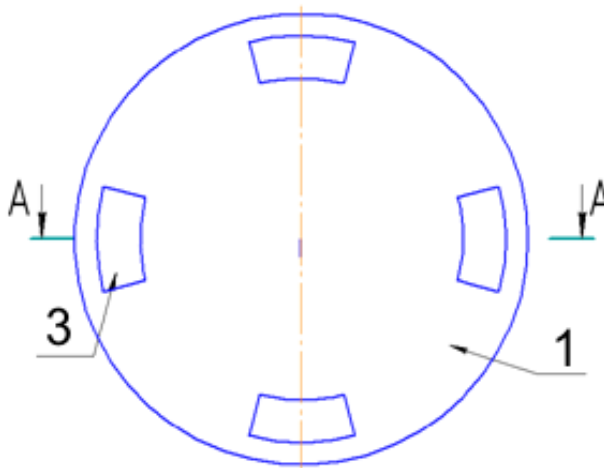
Плавающее покрытие для резервуара (вид снизу)
